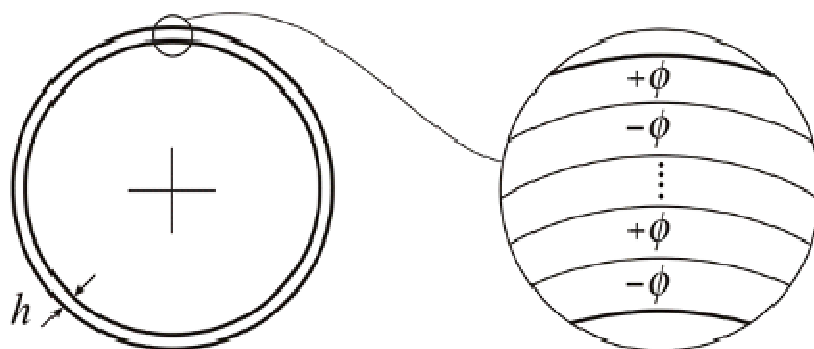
Сечение тонкостенной спицы с круглым поперечным сечением
